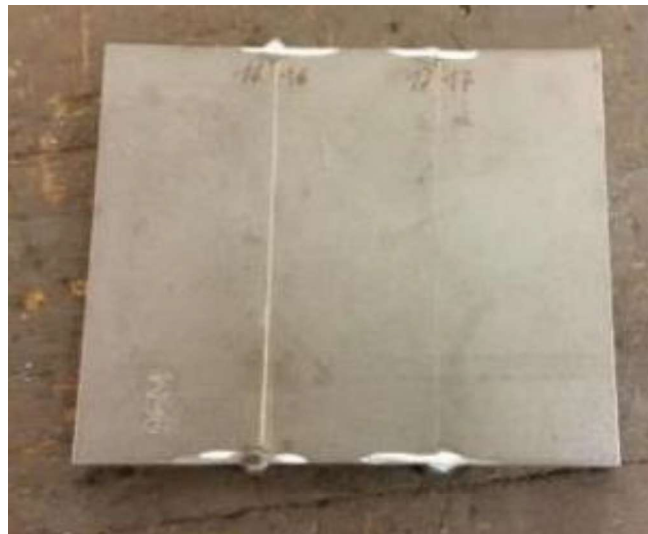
Original 3-Teilige Plattenprobe mit stirnseitigen Schweißpunkten
